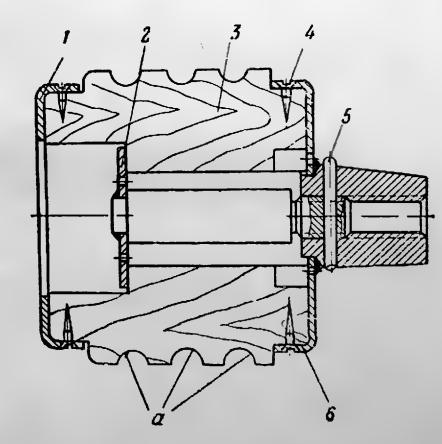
Протирка: I — шайба (1-21); 2 — шайба со шинлькой: 3 колодка (1-20); 4 — шуруп (1-8); 5 — шплинт (1-8); 6 — шайба крепления (C61-5); 6 — кольцевые вы-
